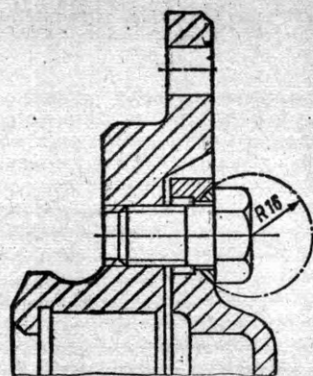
Вариант соединения крышки малой шестерни (со стороны бандажа) с подшипниковым щитом с помощью сферической шайбы или прокладок из мягкого металла
